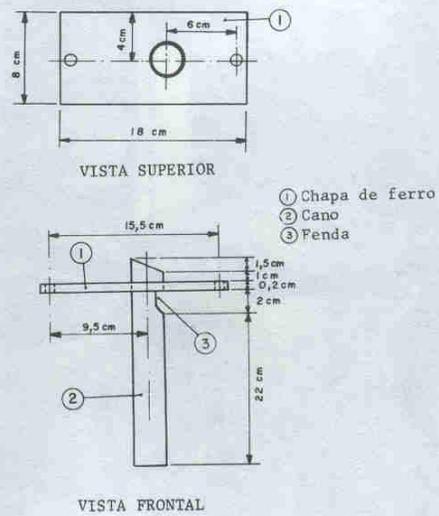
e) Dispositivo II da plantadeira de precisão
